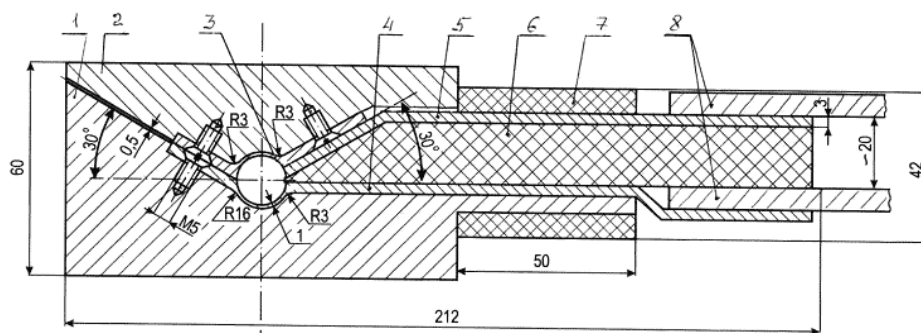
Схема разъемного одновиткового индуктора: 1 - полукорпус (сталь 30ХГСА); 2 - полукорпус (сталь 30ХГСА); 3 – токовод рабочей зоны (бронза БрБ2); 4 – токовод рабочей зоны и МИУ (бронза БрБ2); 5 – токовывод к МИУ; 6 – изолирующая проставка (текстолит); 7 – бандаж (стеклоткань, пропитанная эпоксидным компаундом); 8 - токовыводы установки МИУ 20/5
